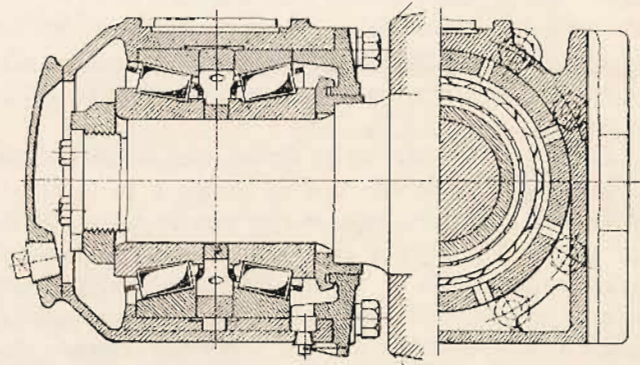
Caja de eje exterior con cojinetes de rodillos cónicos.
